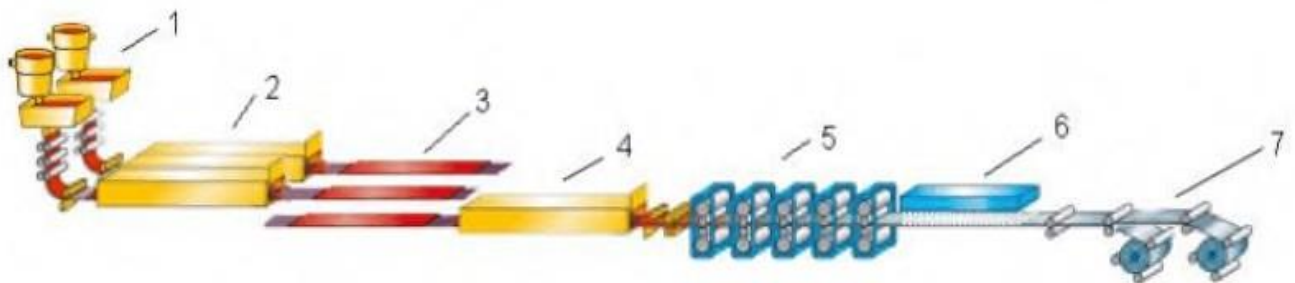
Двоструменевий агрегат CSP для отримання товстих листів: 1 – двохструменева машина безперервної розливки сталі; 2 – прохідна піч; 3 – пристрій поперечного руху металу; 4 – термічна піч; 5 – прокатні кліті; 6 – ділянка охолодження металу; 7 – моталки
